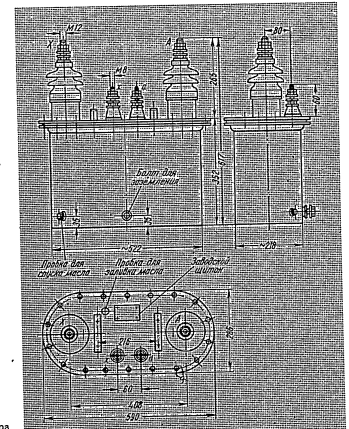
Габаритные размеры трансформатора напряжения типа НОМ-15.
